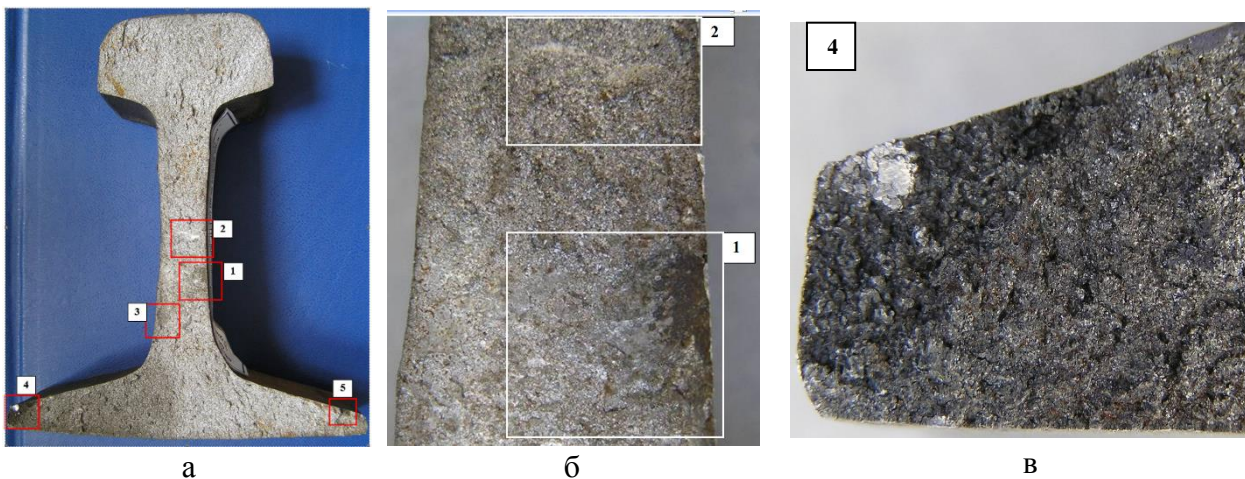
Злам зварної рейки (а), дефекти в шийці (б), та підшви (в) рейки
